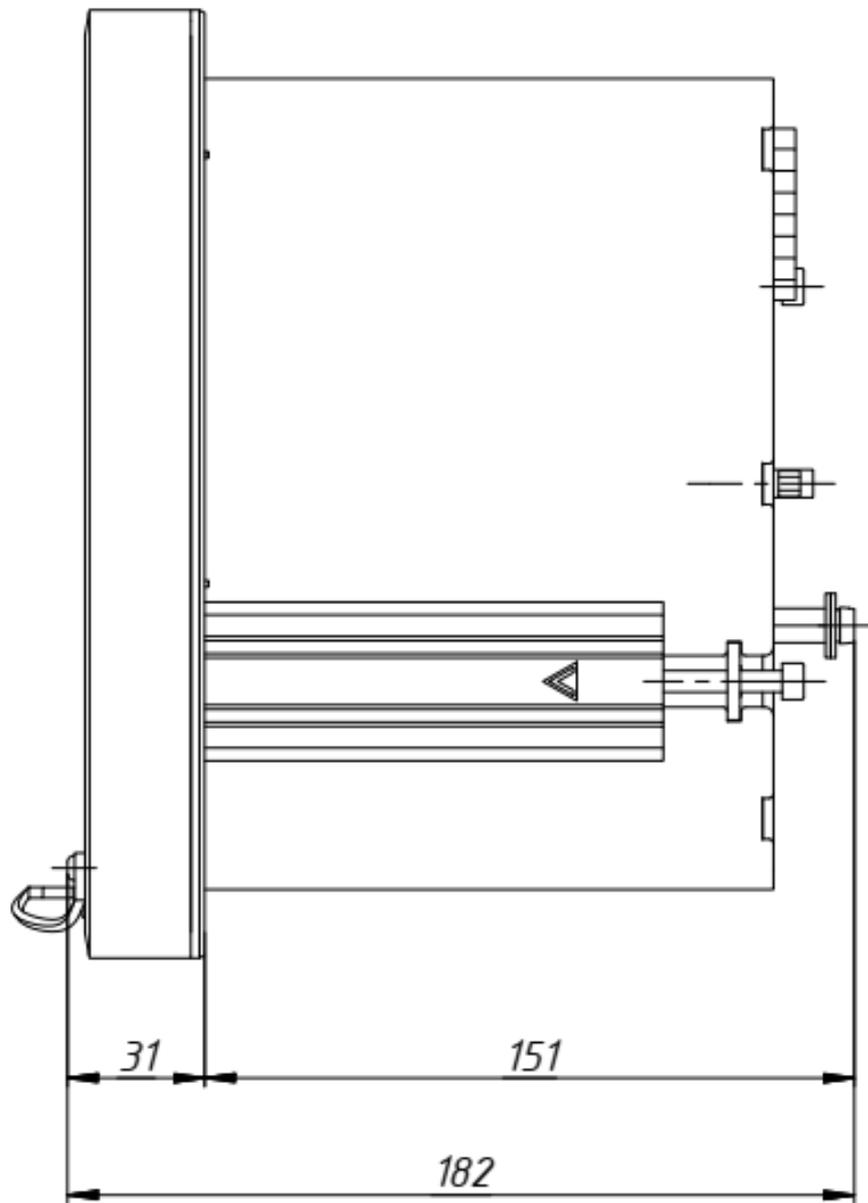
Габаритный чертёж прибора в исполнении Ф1772–1, вид сбоку
